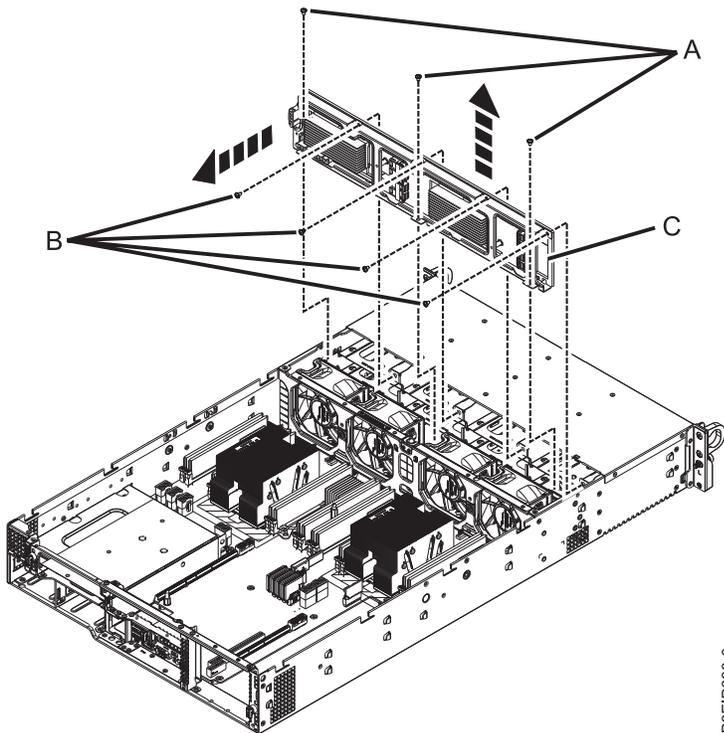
Rückwandplatine des Laufwerks ausbauen und Schrauben entfernen
